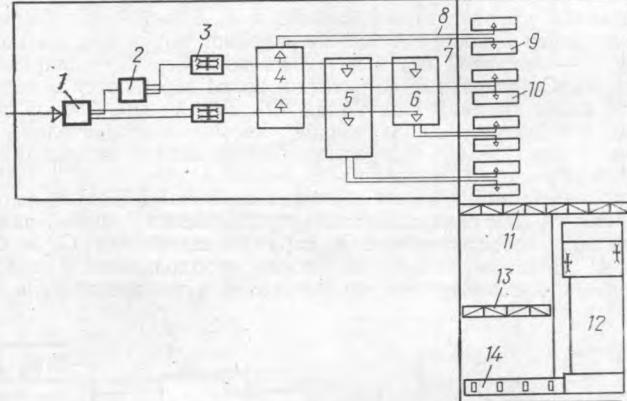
Схема планировки лесопильного завода со смещением карманов-накопителей:
